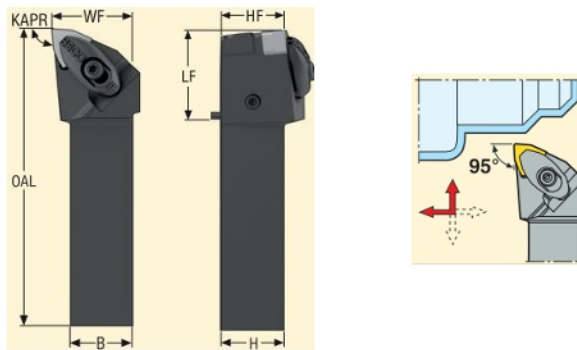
Державка DWLNR/L2525X06JETI [1, с. 214]
